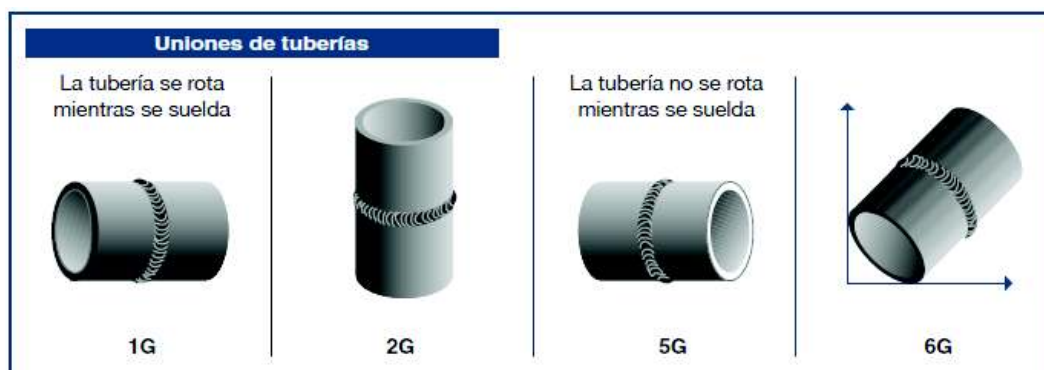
Posiciones de soldadura para uniones de tuberías⁴⁷
